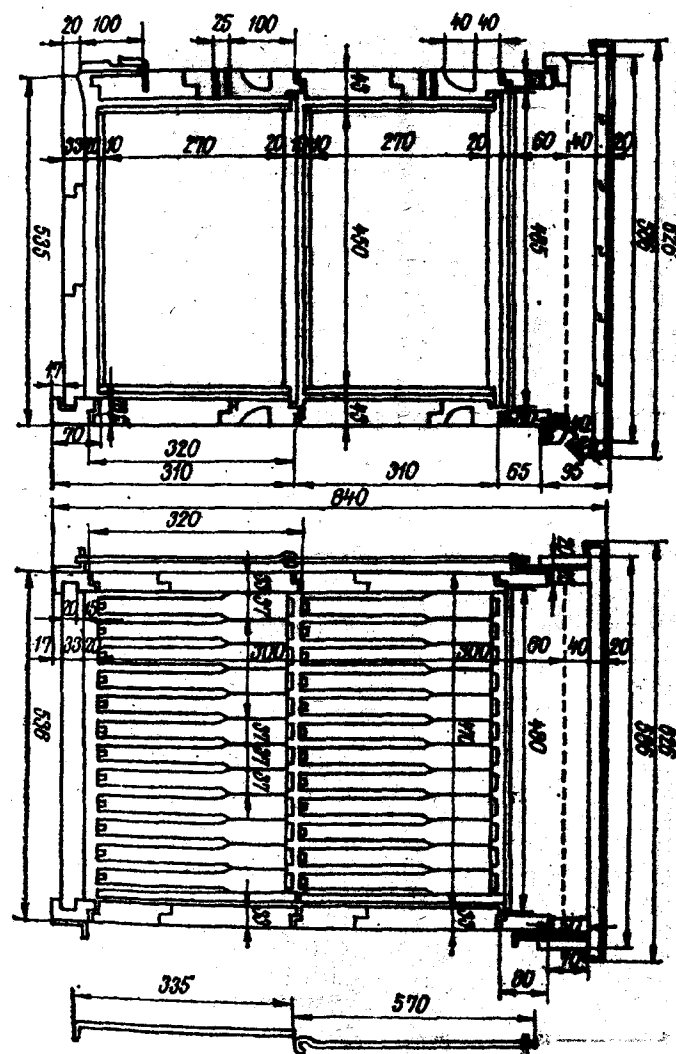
Secțiune longitudinală și transversală în stupul vertical cu două corpuri
